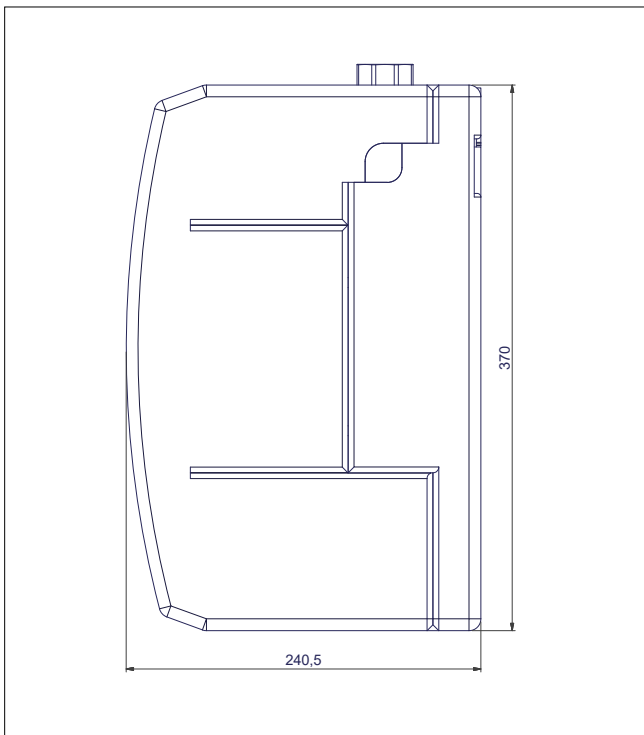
Dimensions des modules hydrauliques avec coquille isolante
